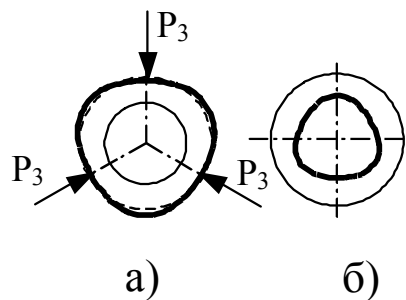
Похибка форми: а – під час обробки; б – після зняття
